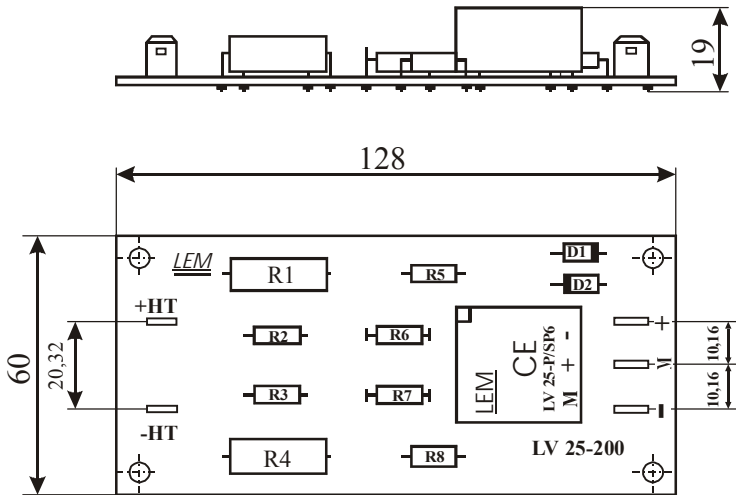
Внешний вид и габаритные размеры датчиков напряжения типа LV 25-200, LV 25-400, LV 25-600, LV 25-600/SP1
